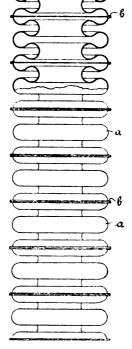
Geschweißter Schlauch aus mehrwelligen Rohrstücken.
